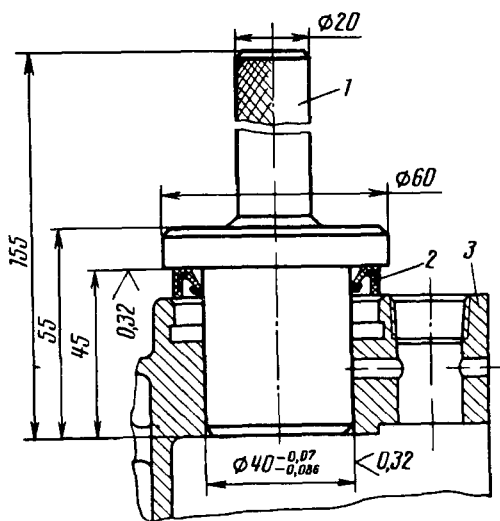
Запрессовка манжеты распределительного вала в головку цилиндров:
